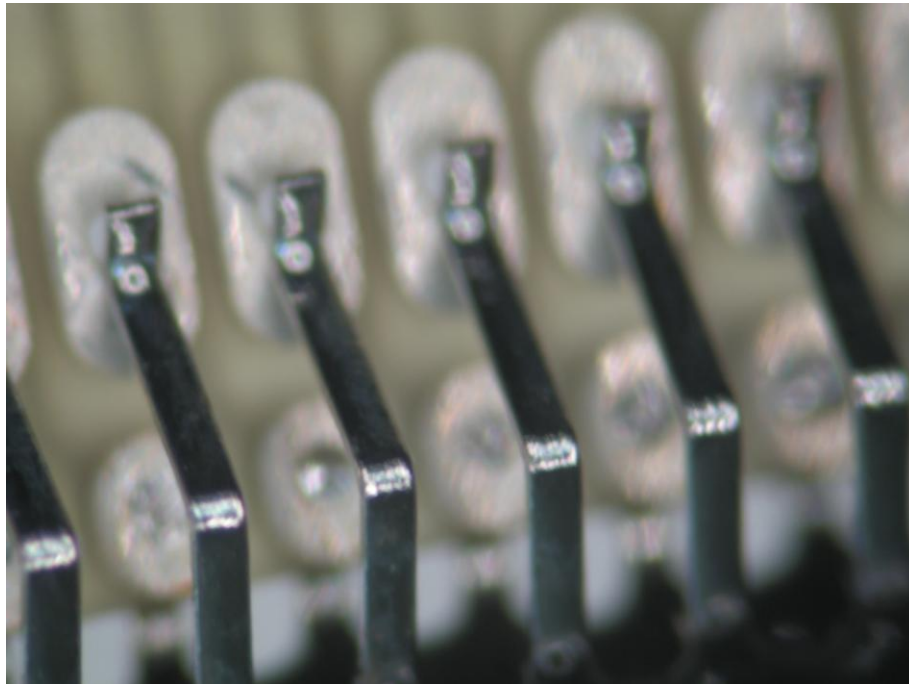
Detalhe do encaixe entre o conector e a placa antes de soldá-los
